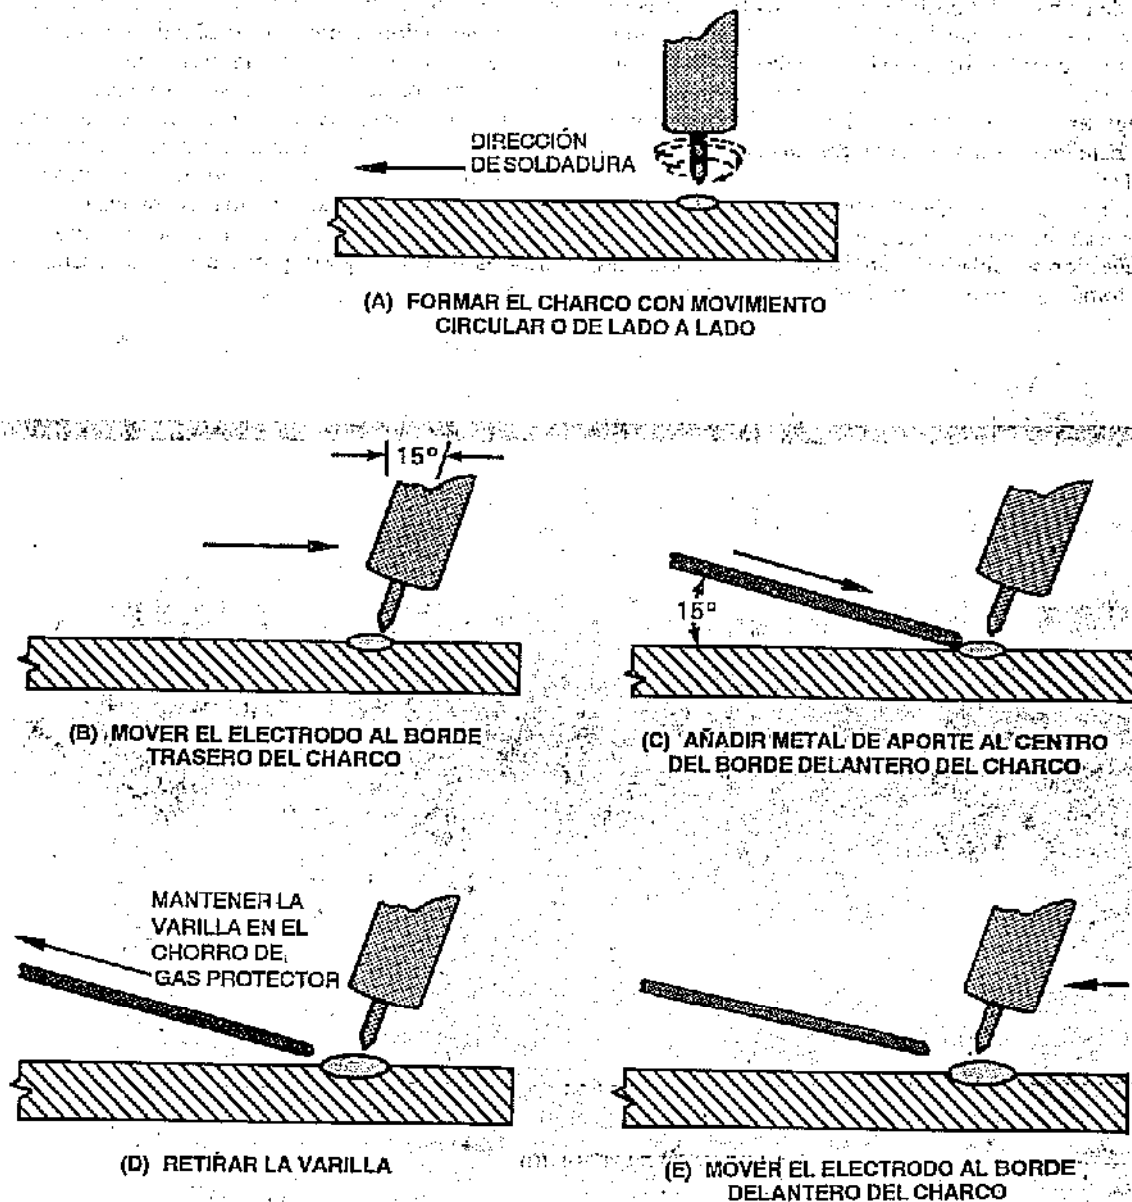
Técnica para soldadura por arco de tungsteno y gas manual
